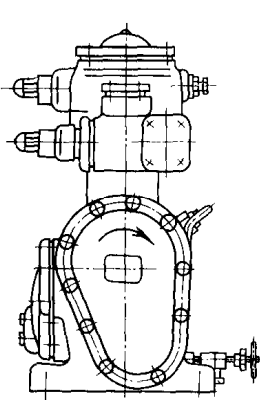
Компресор ФВ22*: сальниковий, вертикальний, 2-х циліндровий
